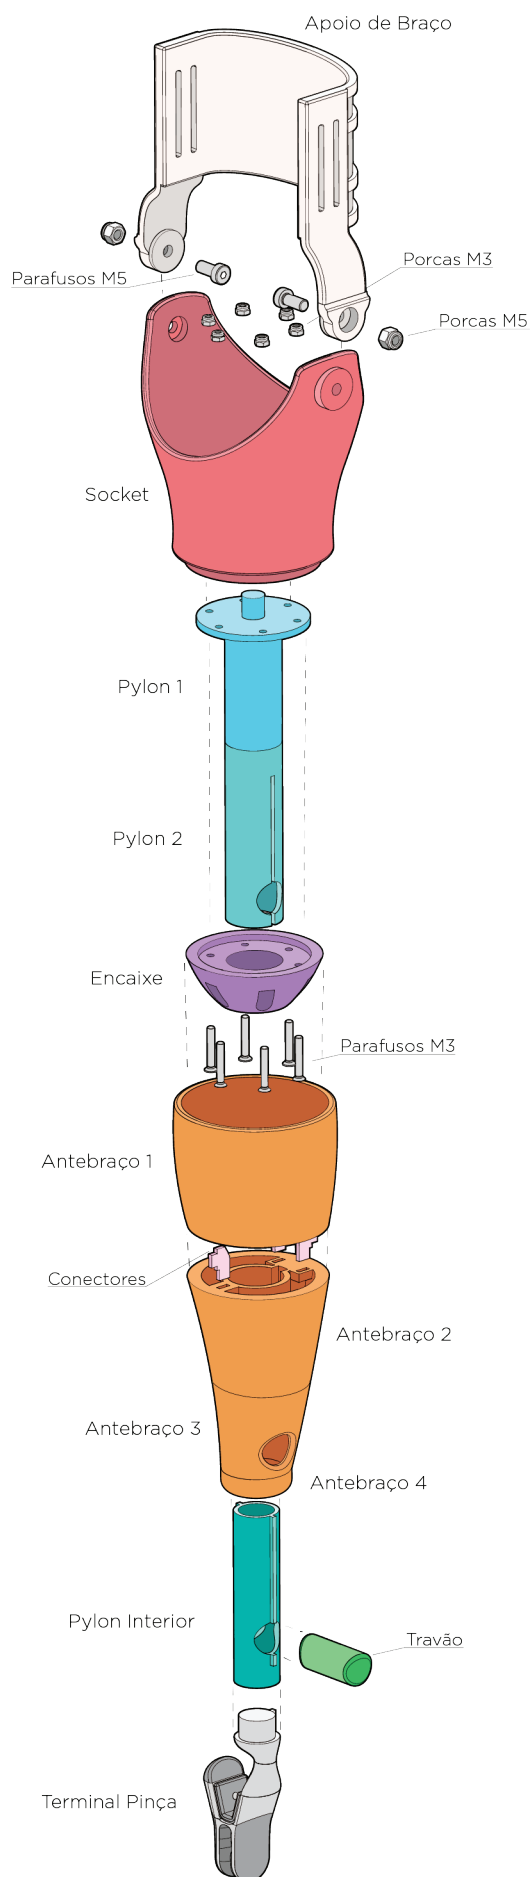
Perspectiva Explodida dos componentes da prótese; Fonte: Investigador (2016)
